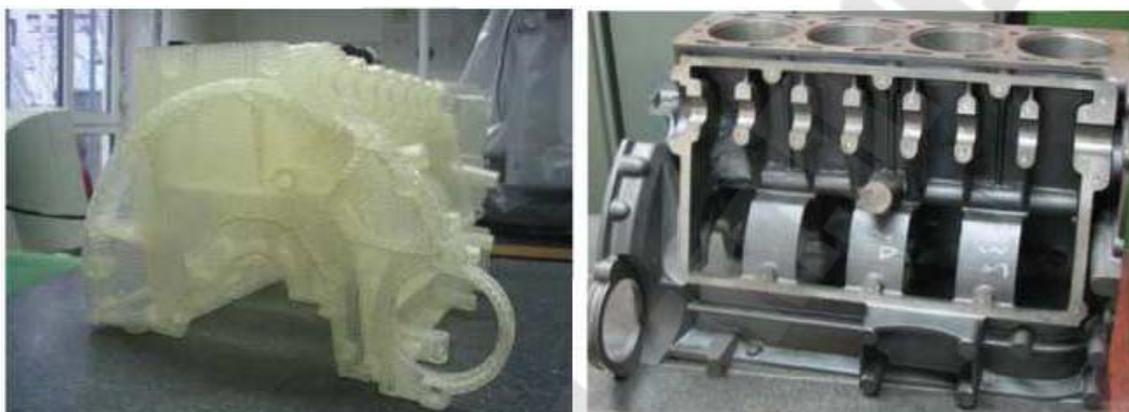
Модель и отливка блока цилиндров из чугуна
